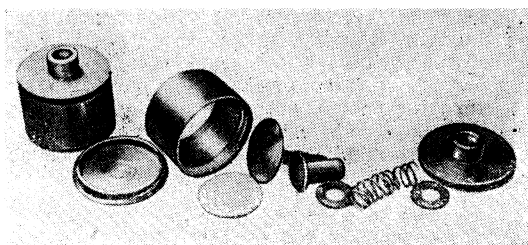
Внешний вид и составные детали армировки преобразователя из керамики титаната бария.
